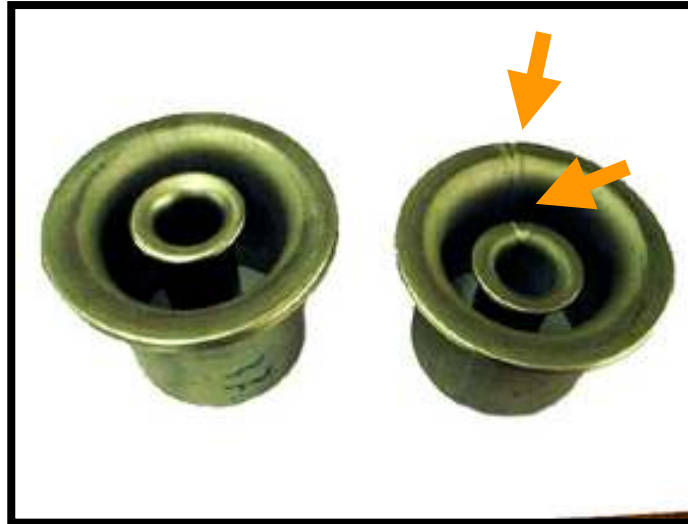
Tubos com e sem costura após ensaios de flangeamento. Setas indicam a solda longitudinal.
